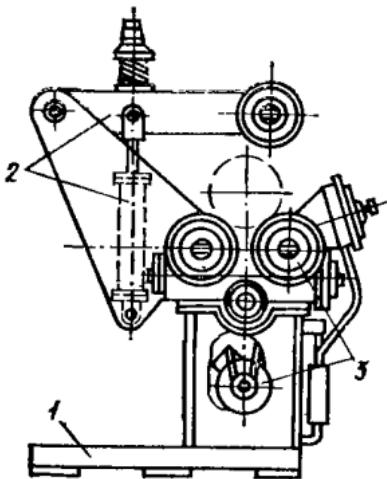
Универсальный фрикционный вращатель УВТ-1 для сварки элементов трубопроводов:
